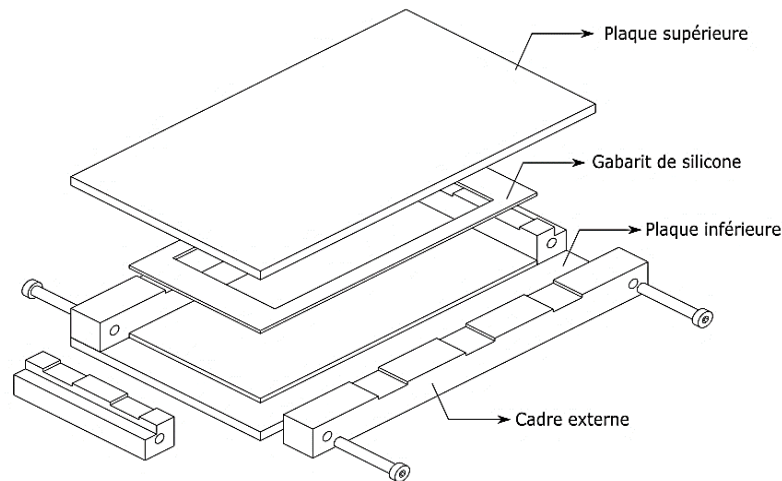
Vue éclatée du moule permettant de produire des spécimens de plaques.
